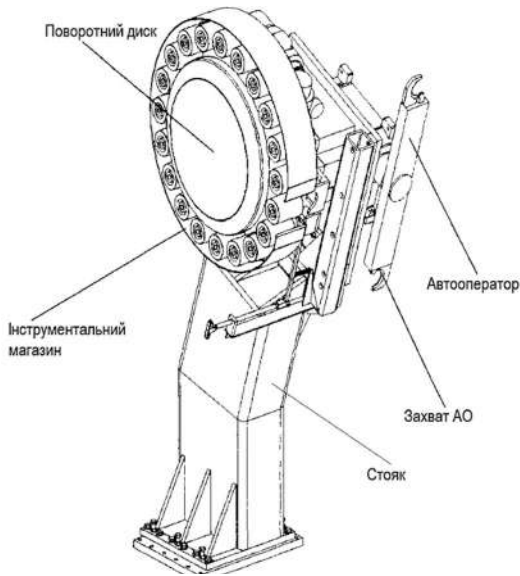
Пристрій автоматичної зміни інструмента
